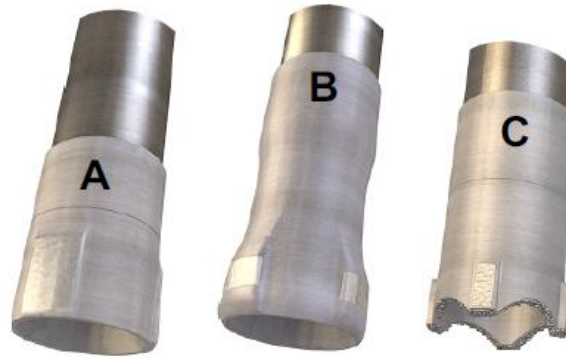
Zapatas de TR: (A). Zapata Guía, (B). Zapata Guía Direccional y (C) Zapata Perforadora. (PETSOC 2004-183).
